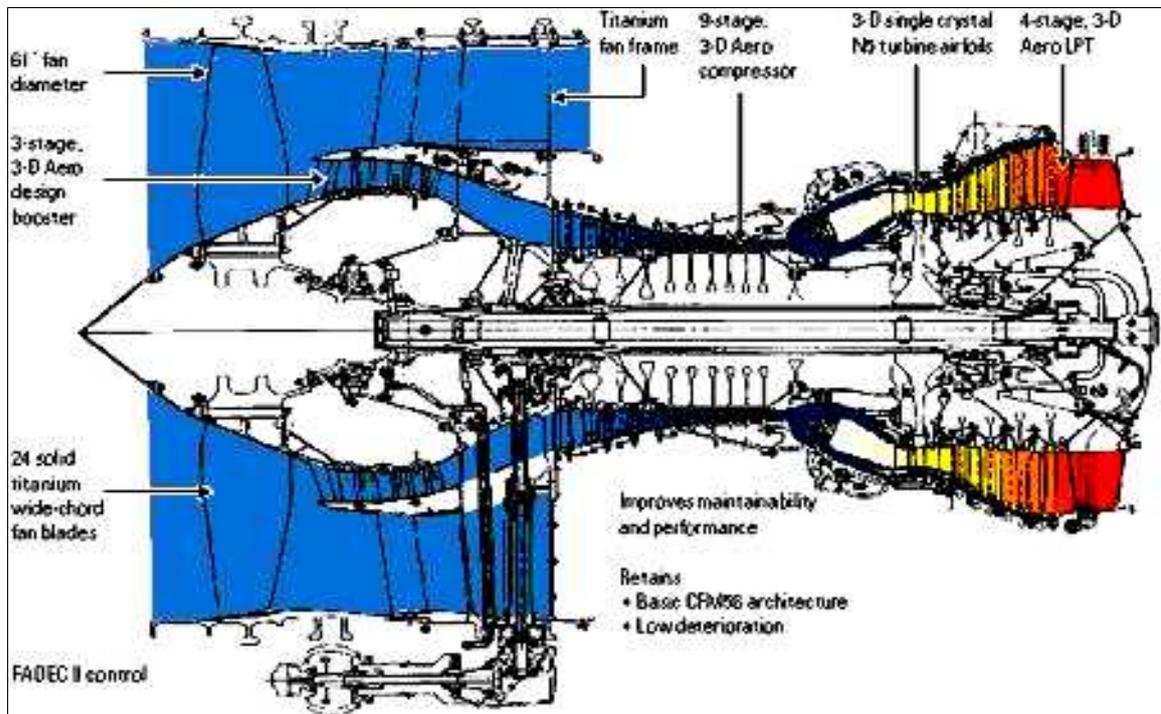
Vue en coupe du moteur CFM56-7B
